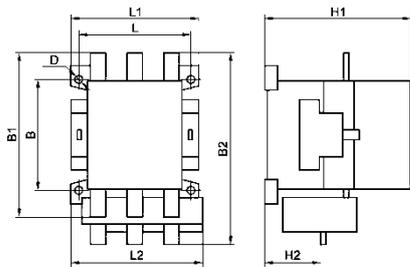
Пускатель неререверсивный ПМ12 100-250А. Степень защиты - IP00
